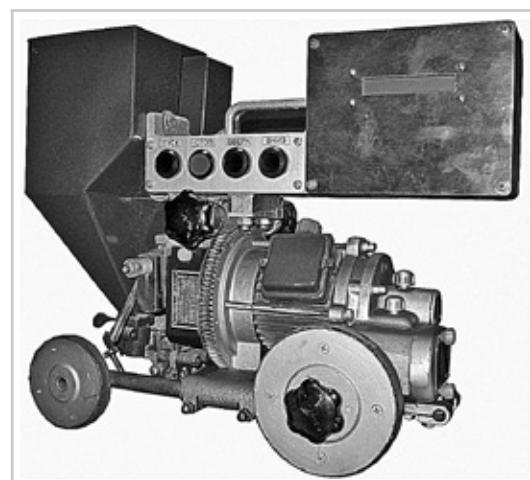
Сварочный автомат АДФ-1002Ц
